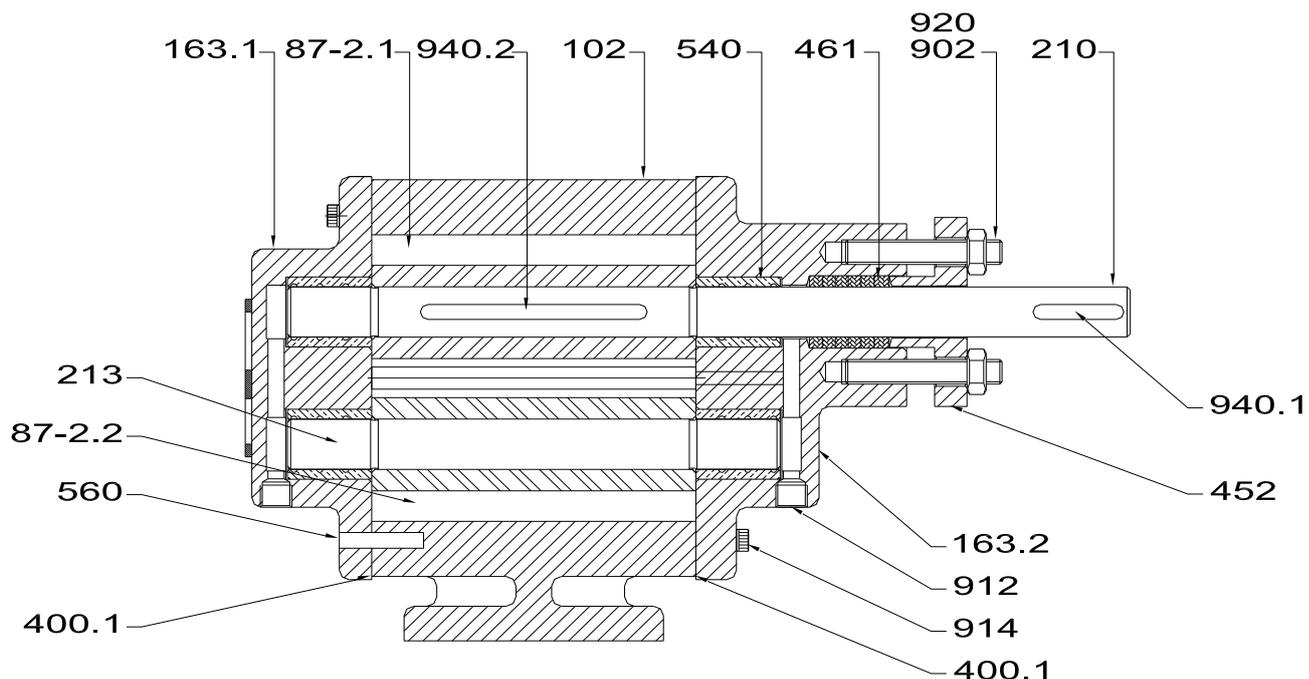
Desenho em Corte bomba FBE 1”D – 1”DA com gaxeta
